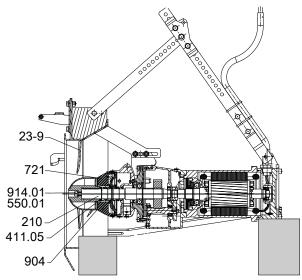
Montaje de la hélice axial; Amaline 500, 600
